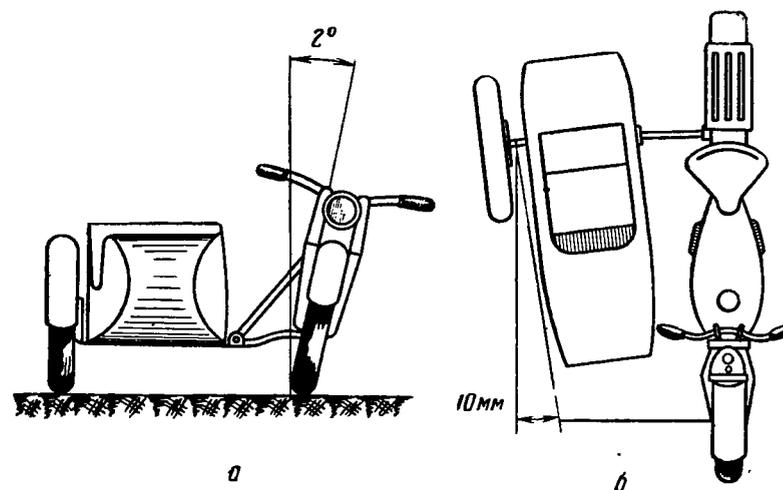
Схема установки бокового прицепа: а — угол наклона мотоцикла; б — сходимость колес.
